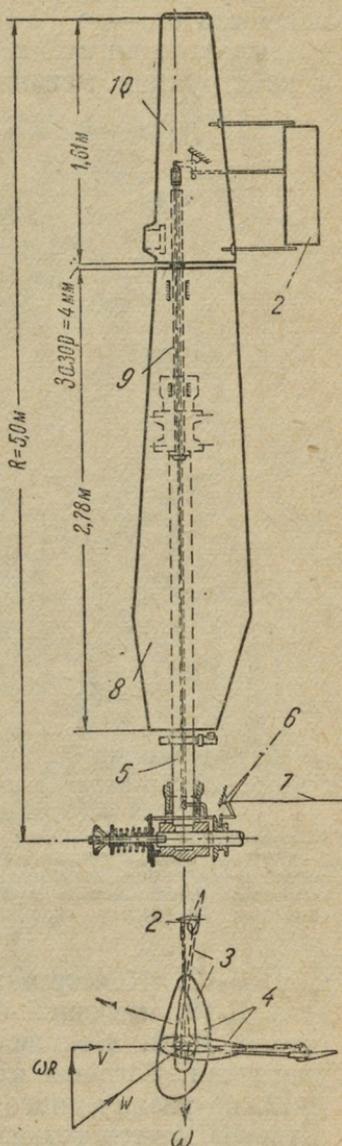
Крыло ветродвигателя ЦВЭИ Д-10 с самоустанавливающейся частью лопасти:
